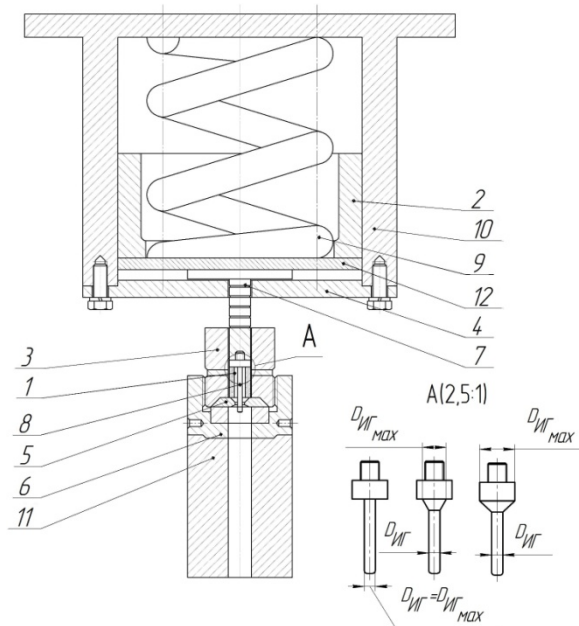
Комплекс прессового инструмента для физического моделирования процесса инерционного прессования труб: 1 – заготовка; 2 – центрирующая втулка; 3 – контейнер; 4 – крышка стакана; 5 – матрица; 6 – матрицедержатель; 7 – пресс-штемпель; 8 – пресс-игла; 9 – пружина сжатия; 10 – стакан; 11 – стойка опорная; 12 – пресс-шайба
